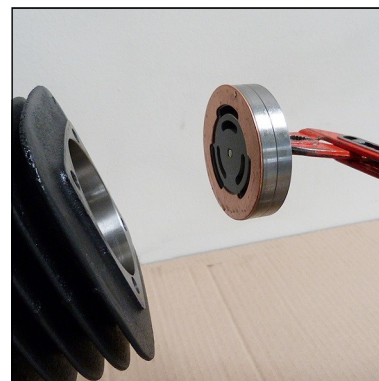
Neues Saug- / Druckventil in Zylinder ausgerichtet einsetzen
